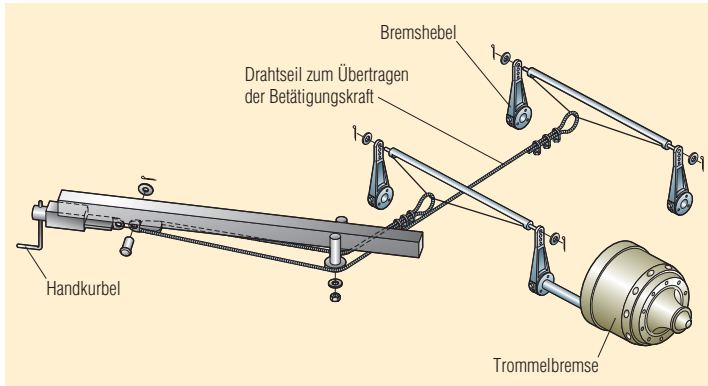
Aufbau einer mechanischen Feststellbremse am Anhänger.
